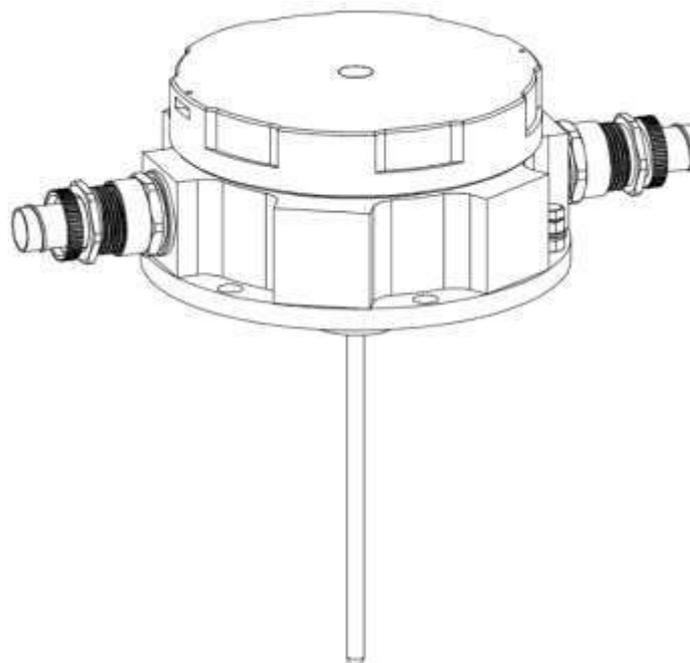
Внешний вид извещателя пожарного взрывозащищенного.
